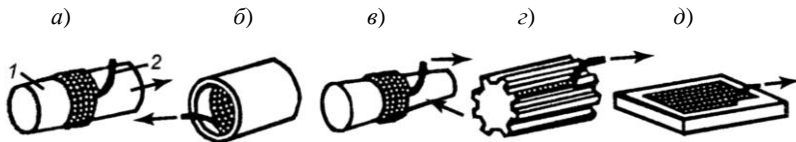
Схемы вибродуговой наплавки изношенных поверхностей:
